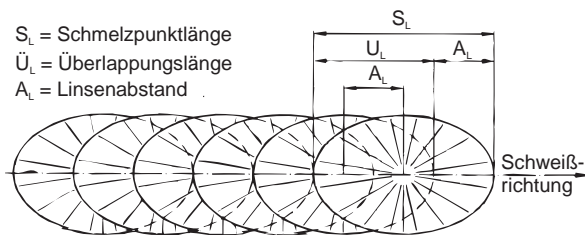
Aufbau der Schweißnaht aus einzelnen Schweißpunkten [2]
